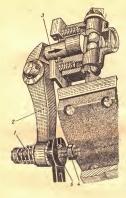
Регулировка привода ручного тормоза автомобили ГАЗ-51А:
